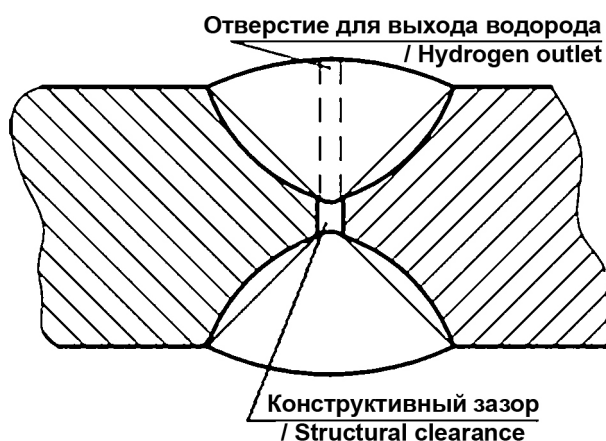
Соединение полости конструктивного зазора сварного шва с атмосферой
